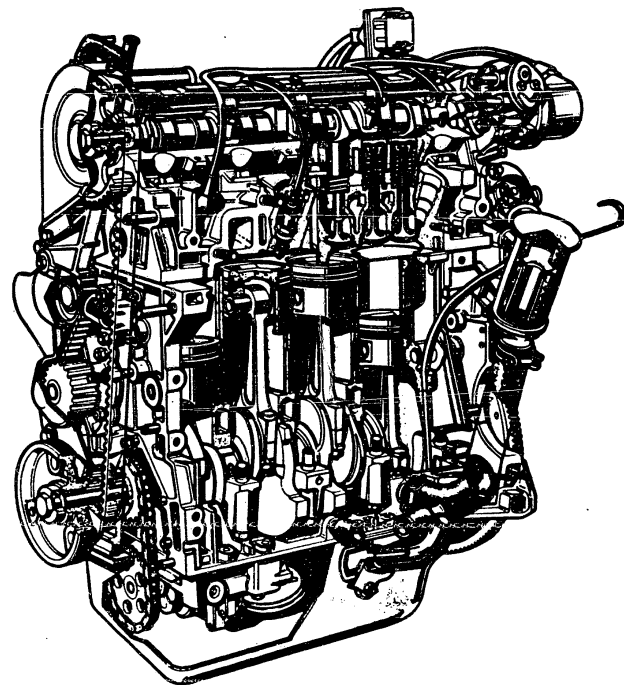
Das moderne Vierzylindertriebwerk weist einen hohen Leichtmetallanteil auf. Die Zahnriemengetriebene Nockenwelle sorgt für den Antrieb von Zündverteiler und Benzinpumpe. Die Ventile werden über Tassenstößel betätigt, die Kolben laufen in nassen Büchsen.
